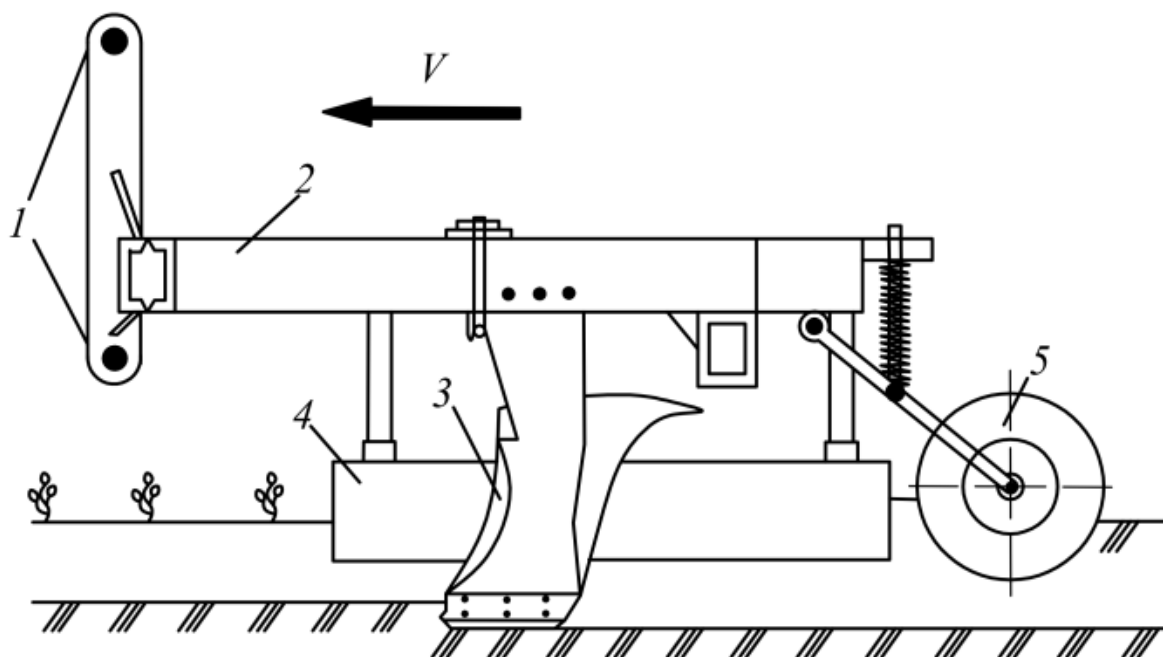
Схема устройства, оборудованного уплотнительным катком
